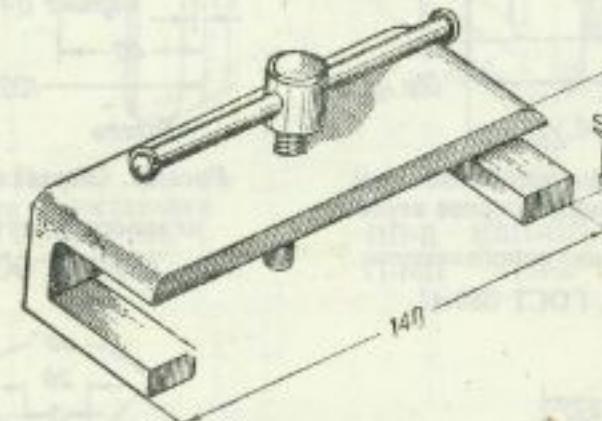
Приспособление для правки станин рамы Д-ПП ПМ-15.
